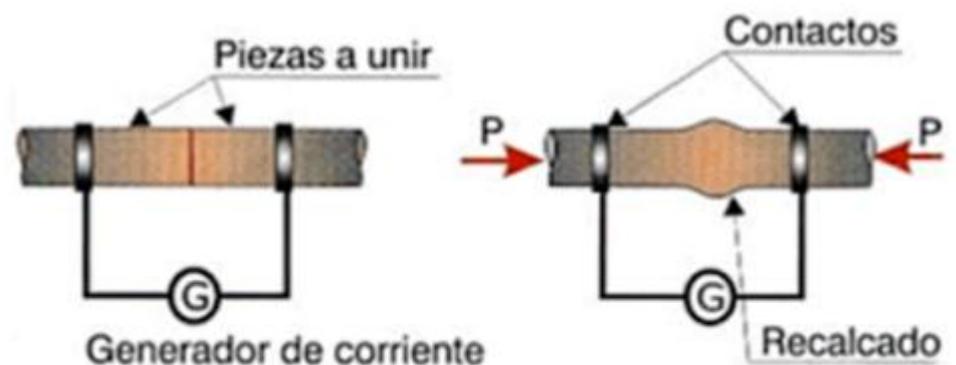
Esquema de soldadura por recalado. [3]
